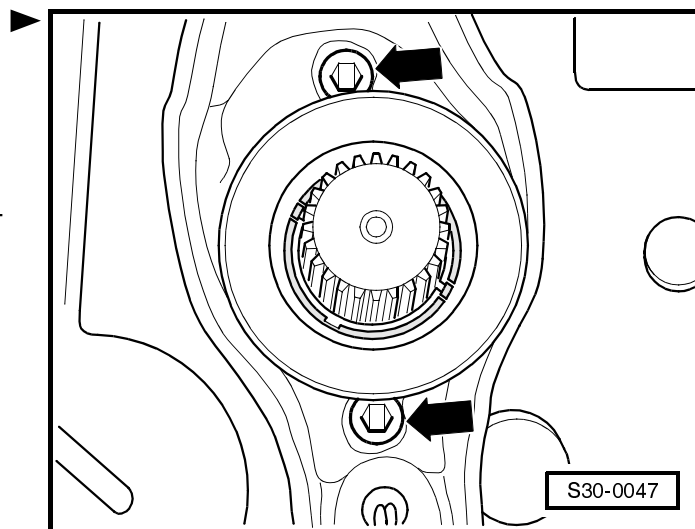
Demontáž a montáž vypínací páky s vypínacím ložiskem spojky a vodicím pouzdem pro vypínací ložisko spojky
